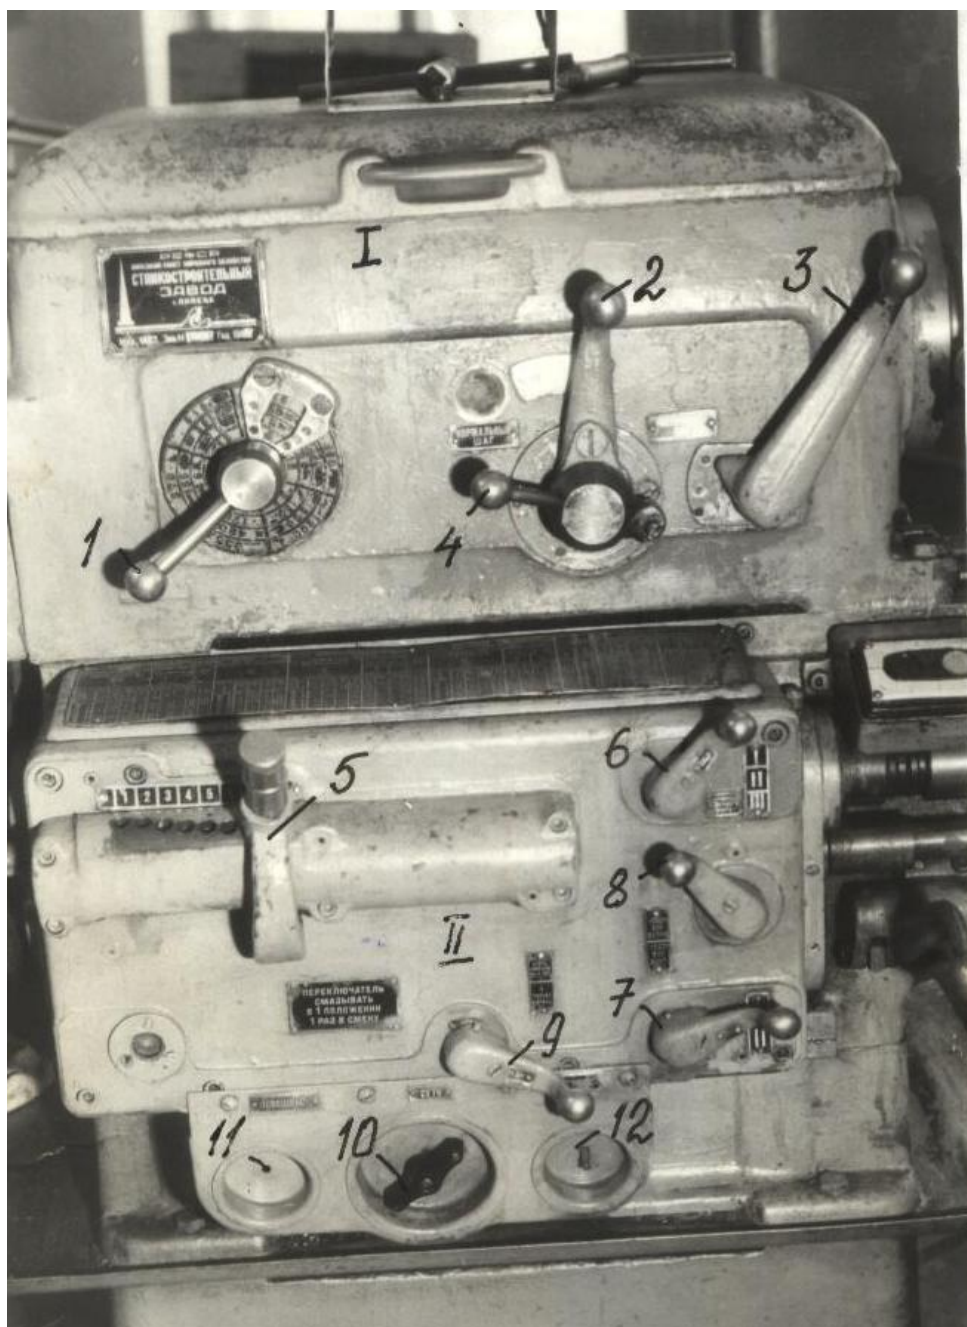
Передняя бабка и коробка подач: I – передняя бабка; II – коробка подач; 1, 2, 3 – рукоятки установки требуемой частоты вращения шпинделя; 4 – рукоятка установки увеличенного шага резьбы; 5, 6, 7, 9 – рукоятки установки требуемой величины подачи и шага резьбы; 8 – рукоятка включения ходового винта и ходового валика; 10 – переключатель подключения и отключения станка от электросети; 11 – включатель освещения; 12 – включатель насоса
